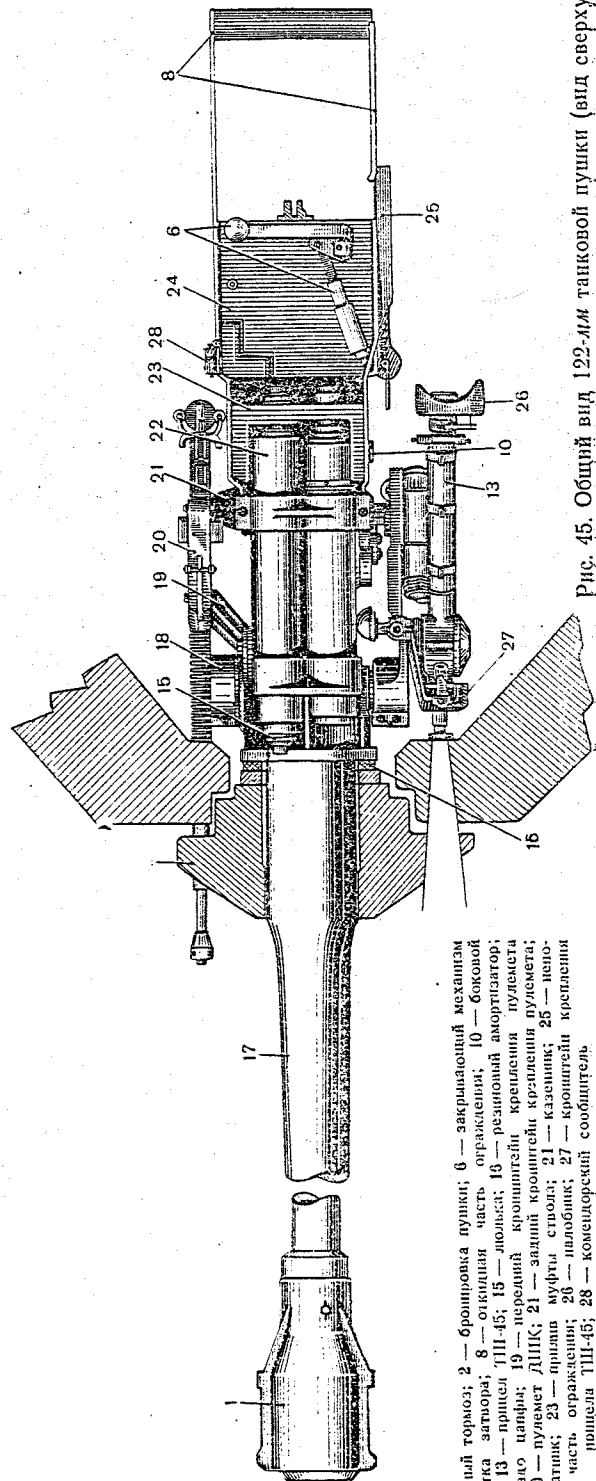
Общий вид 122-мм танковой пушки (вид сверху):
